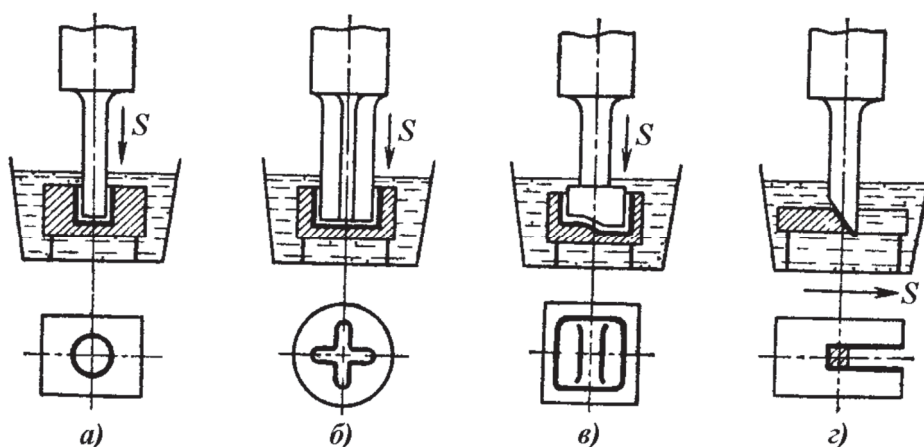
Демонстрація схеми ультразвукової обробки поверхонь: *а*) і *б*) – прошивання циліндричного та фасонного отворів; *в*) – обробка внутрішньої порожнини; *г*) – розрізання
